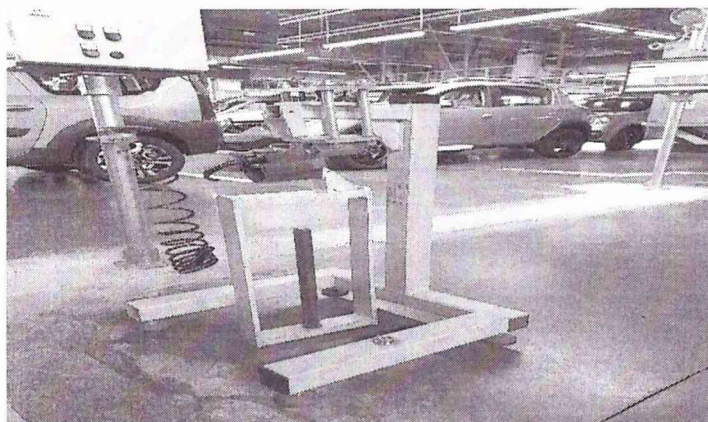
Установка датчика измерений усилий на рукоятке ручного тормоза и калибровочных грузов на калибровочное приспособление
